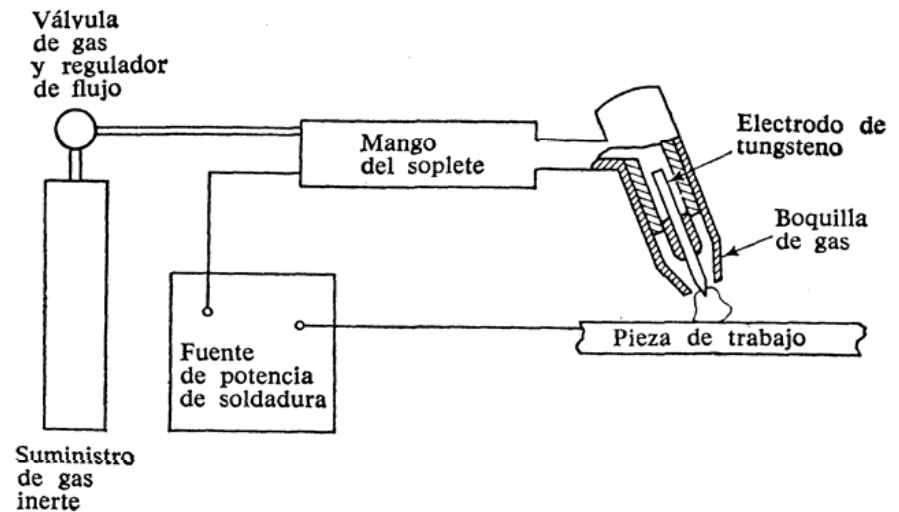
Equipo de soldadura de gas inerte con tungsteno.
